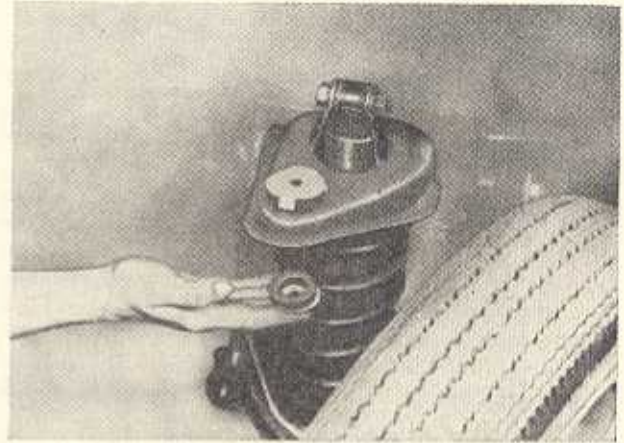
Hintere Karosseriebefestigung, Baumuster 353
